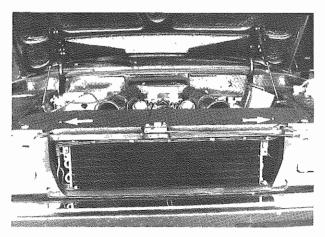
Viti fissaggio guaina copriradiatore Screws for radiator shield
